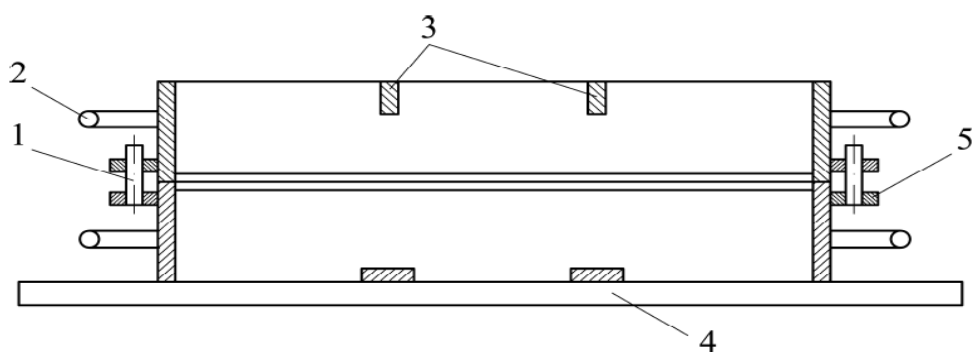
Опоки: 1 - штыри; 2 - ручки; 3 - ребра; 4 - подопочная плита; 5 – ушки
